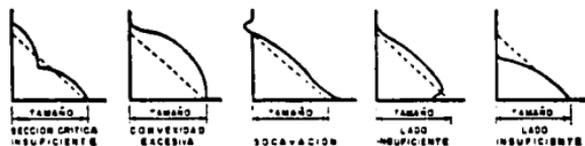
c) Perfiles defectuosos en soldadura de filete.
